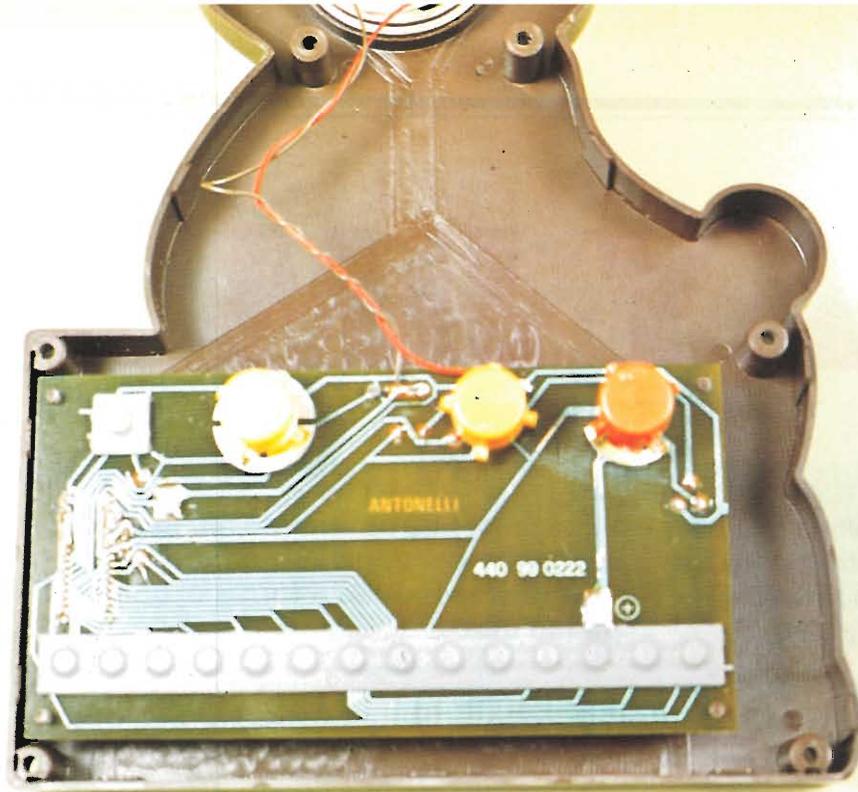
Vista interna dello strumento, si noti il montaggio del corpo dei pulsanti.
